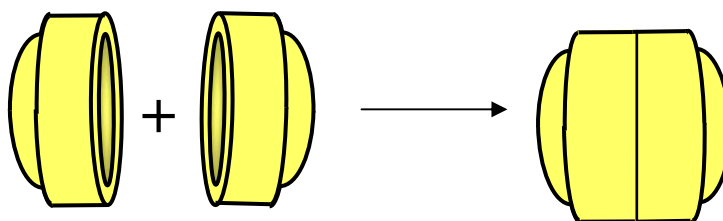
Empilhamento face côncava – face côncava (“void”)
